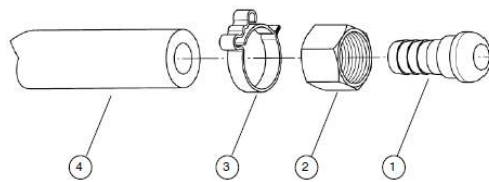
Montaje porta-gomas sobre tubería. (Fuente: BRC Gas Equipment)
